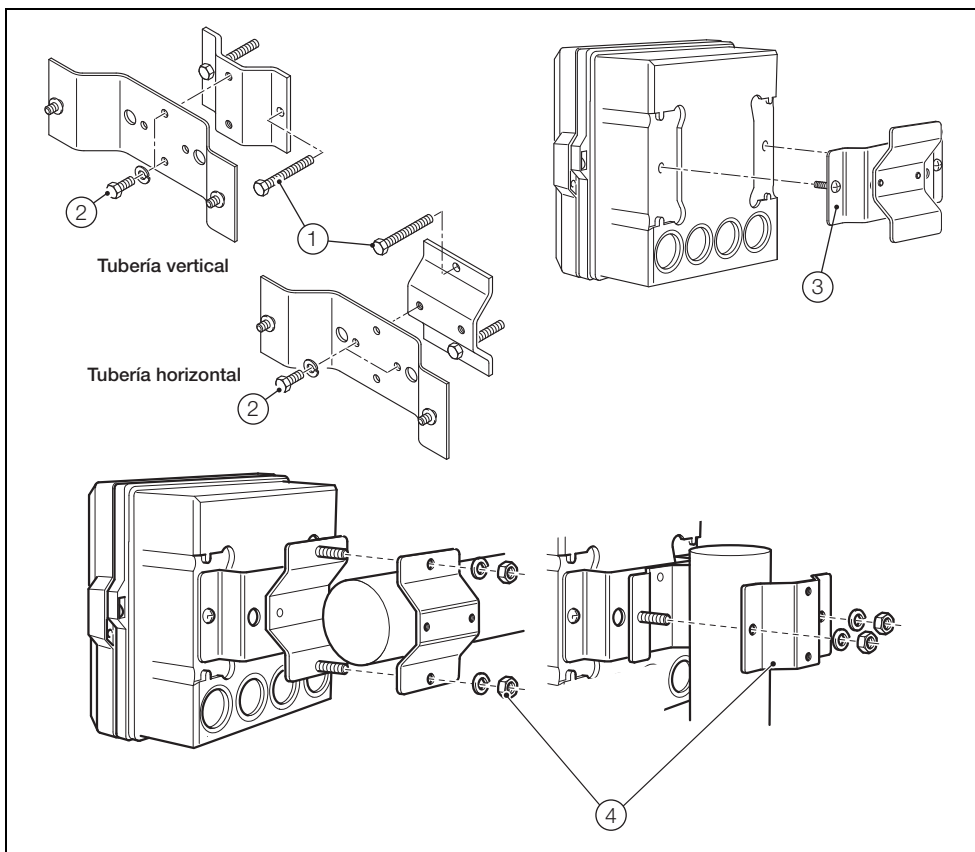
Instalación del instrumento – Montaje en tubería (opcional)
